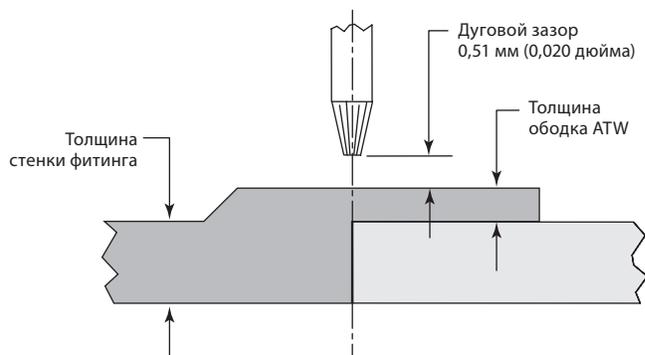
Сварное соединение, полученное способом автоматической сварки встык
